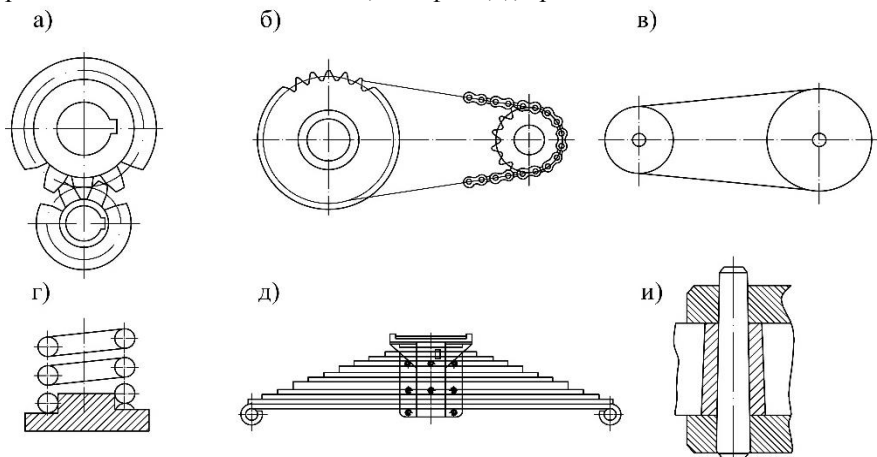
Типовые передачи и детали механического оборудования
